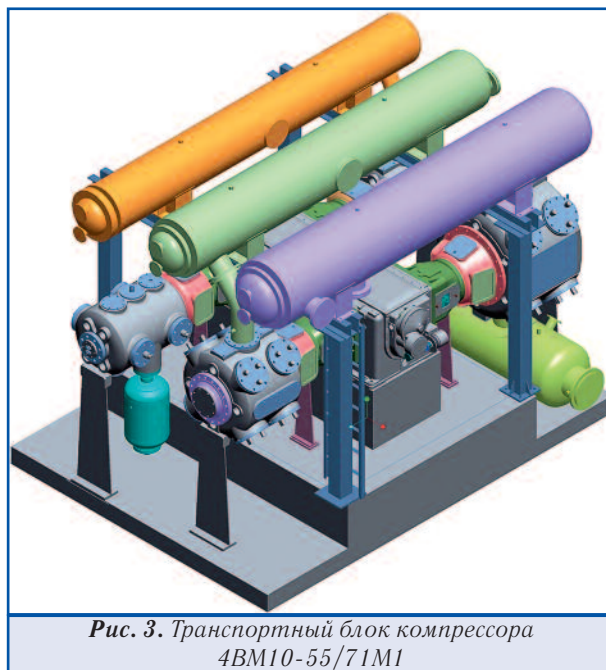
Транспортный блок компрессора 4ВМ10-55/71М1
